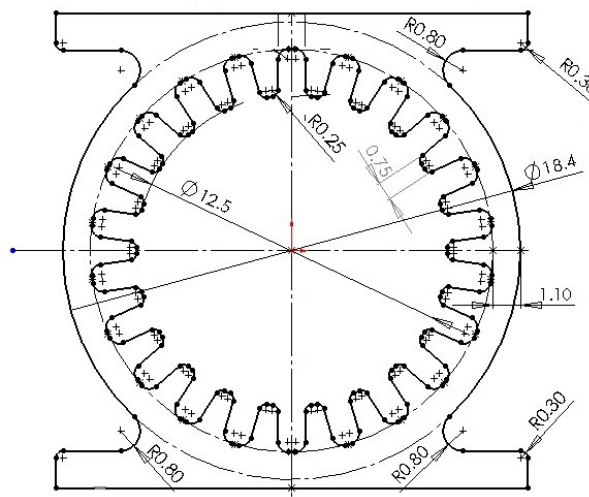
Perfil de um Tubo de Calor Ranhurado
